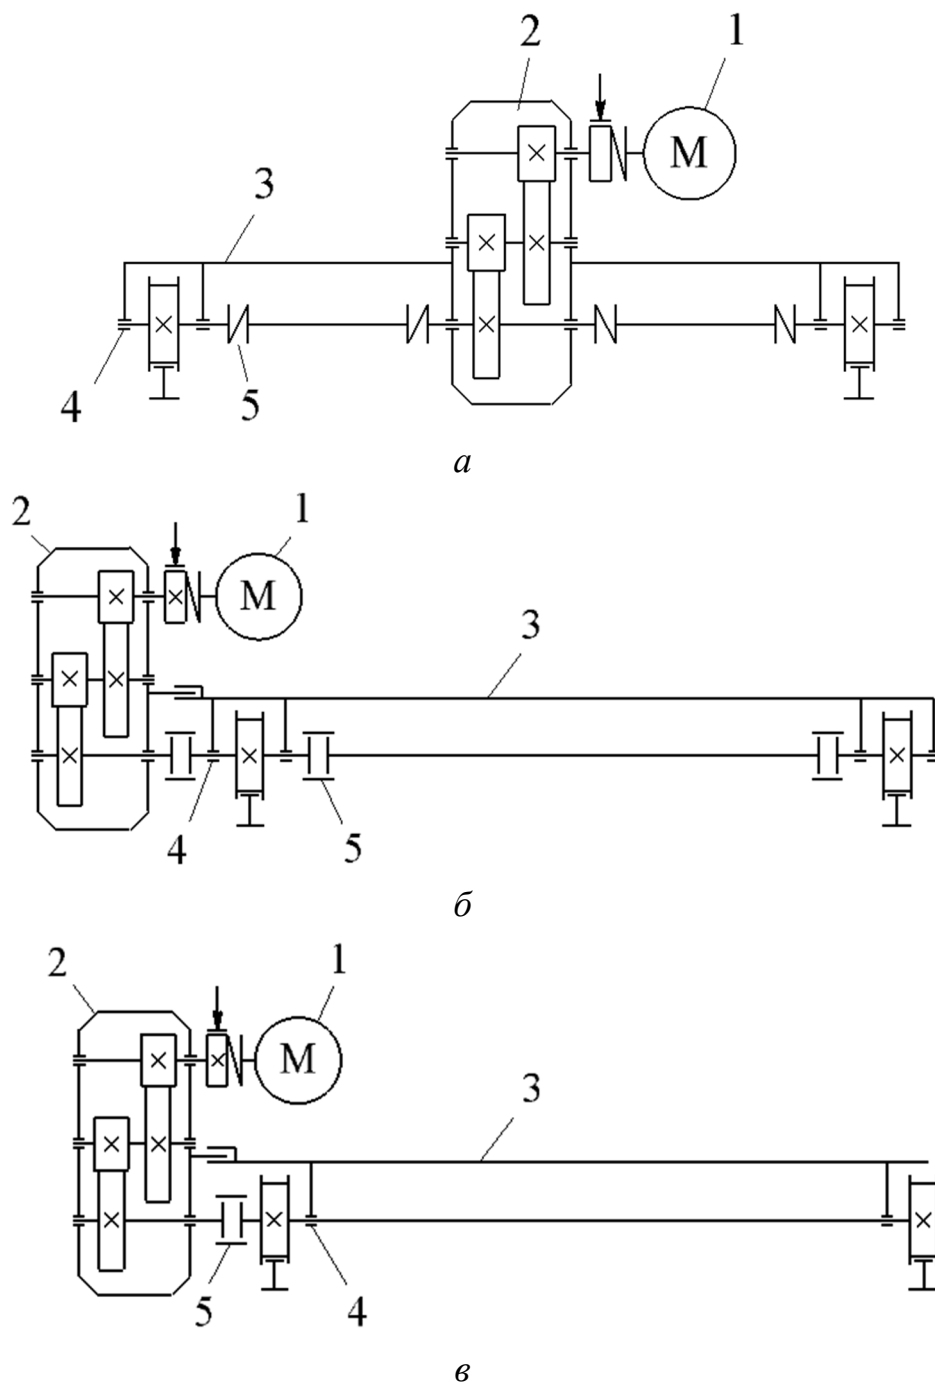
Схемы механизмов передвижения тележки: *а* — с центральным приводом; *б* — с консольным расположением привода; *в* — с общим проходным валом; 1 — электродвигатель; 2 — редуктор; 3 — рама тележки; 4 — букса; 5 — муфта
